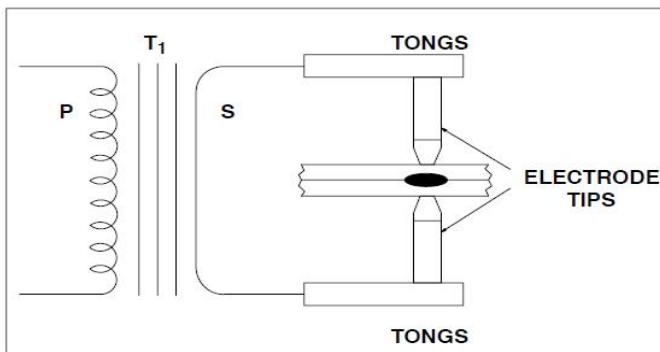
Machine de soudage par points par résistance avec travail
